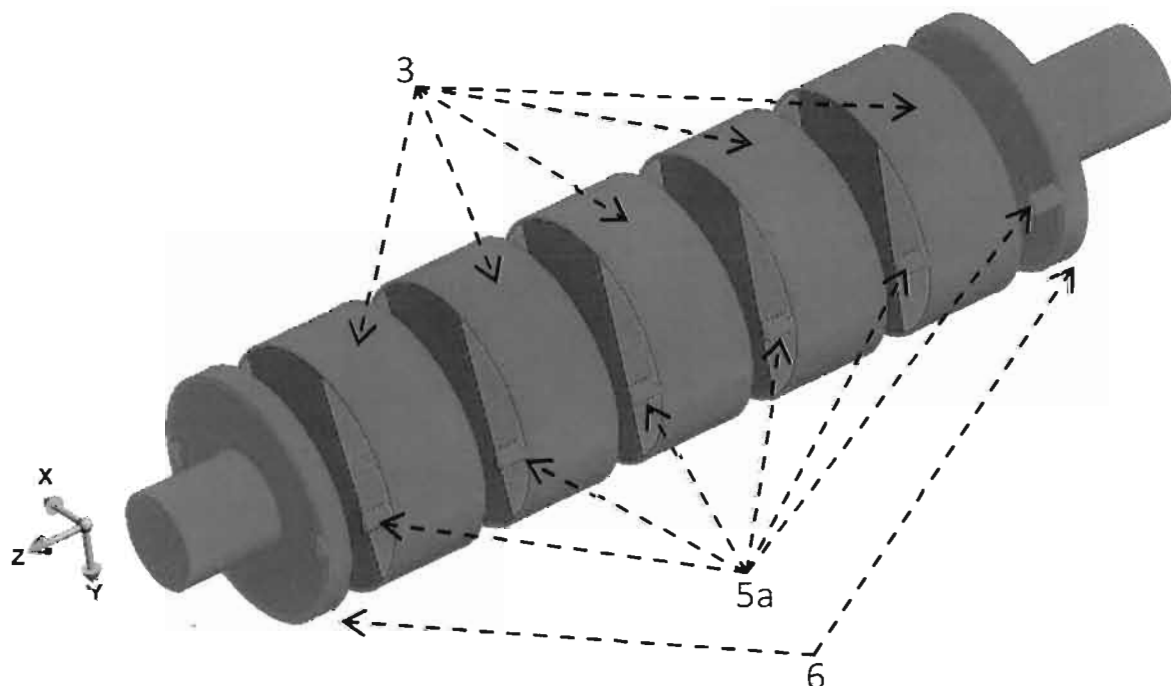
Vedere 3D a rotorului 'explodat' modular, cu tole axiale și tub nemagnetic de consolidare.
